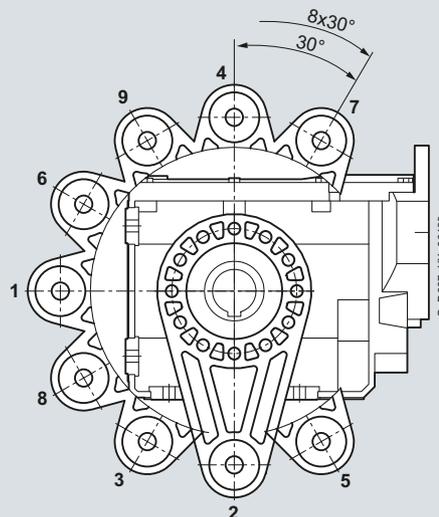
Kegelradgetriebe B in Aufsteckausführung
